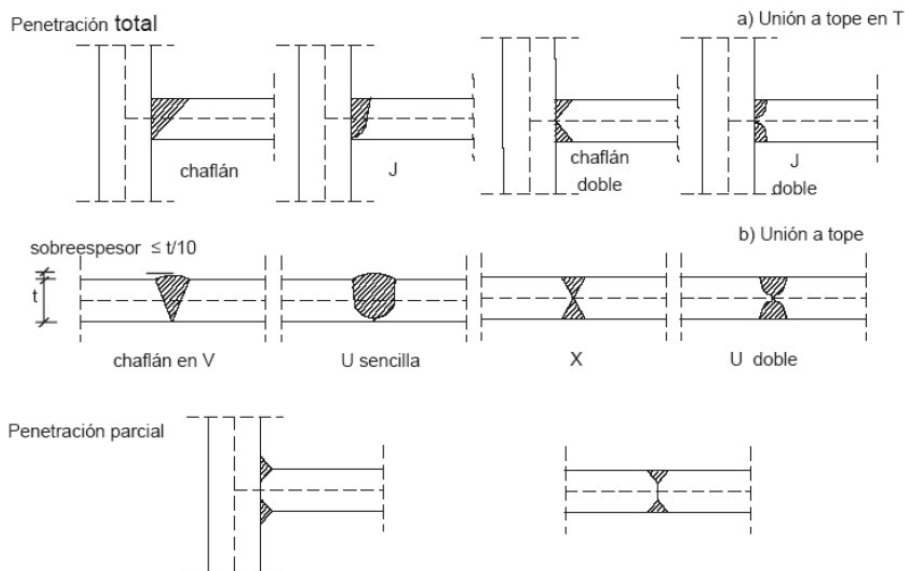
Soldadura de penetración, también conocida como soldadura a tope, y formas de preparación.
